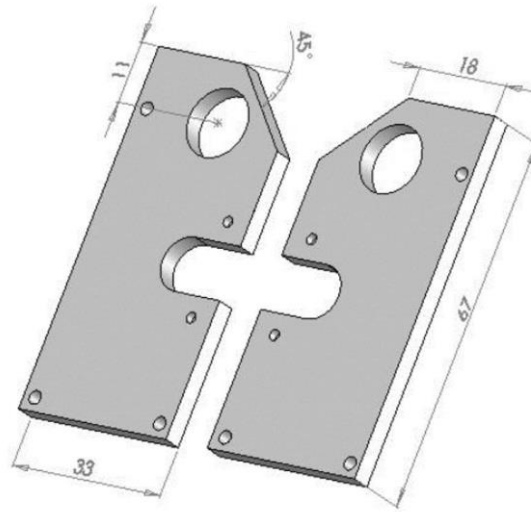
Dispositivo anti-flambagem para corpos de prova C(T). Dimensões em milímetros
